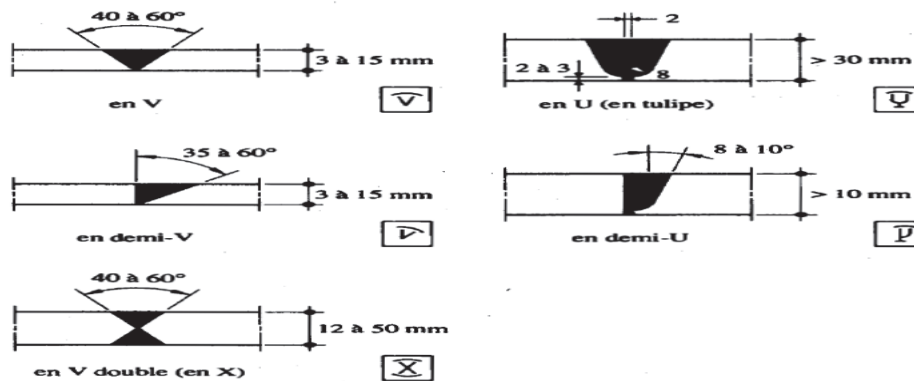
Exemple des soudures bout à bout complètement pénétrées
